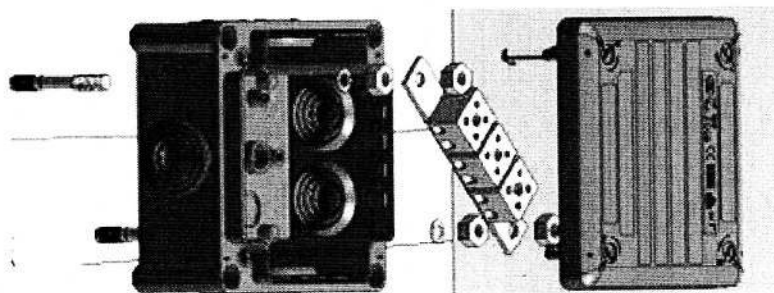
Схема монтажа коробки огнестойкой на бетонное основание.
